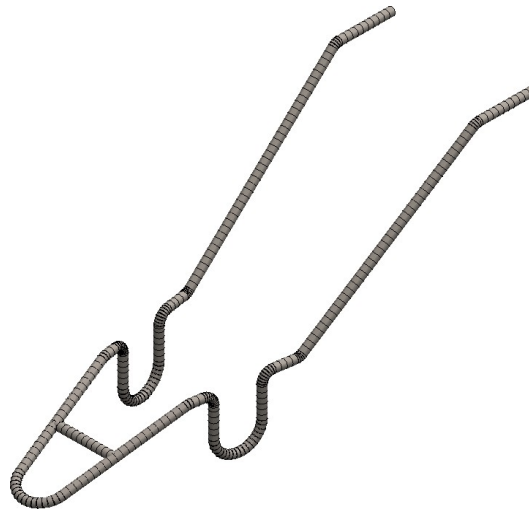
Malla de elementos viga aplicada en la estructura portante o chasis
